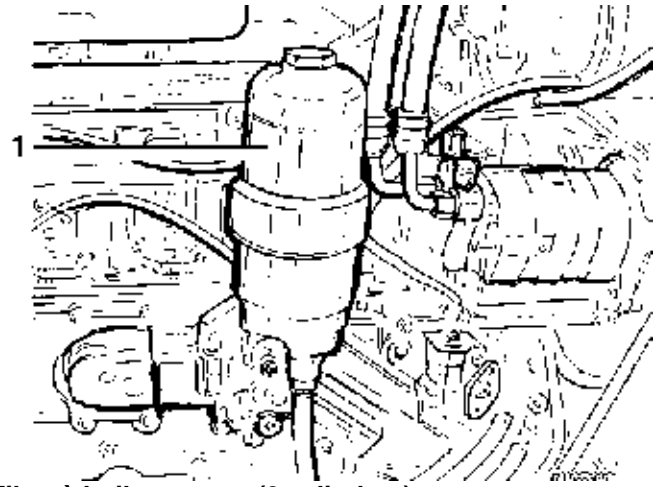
Filtre à huile moteur (6 cylindres)
